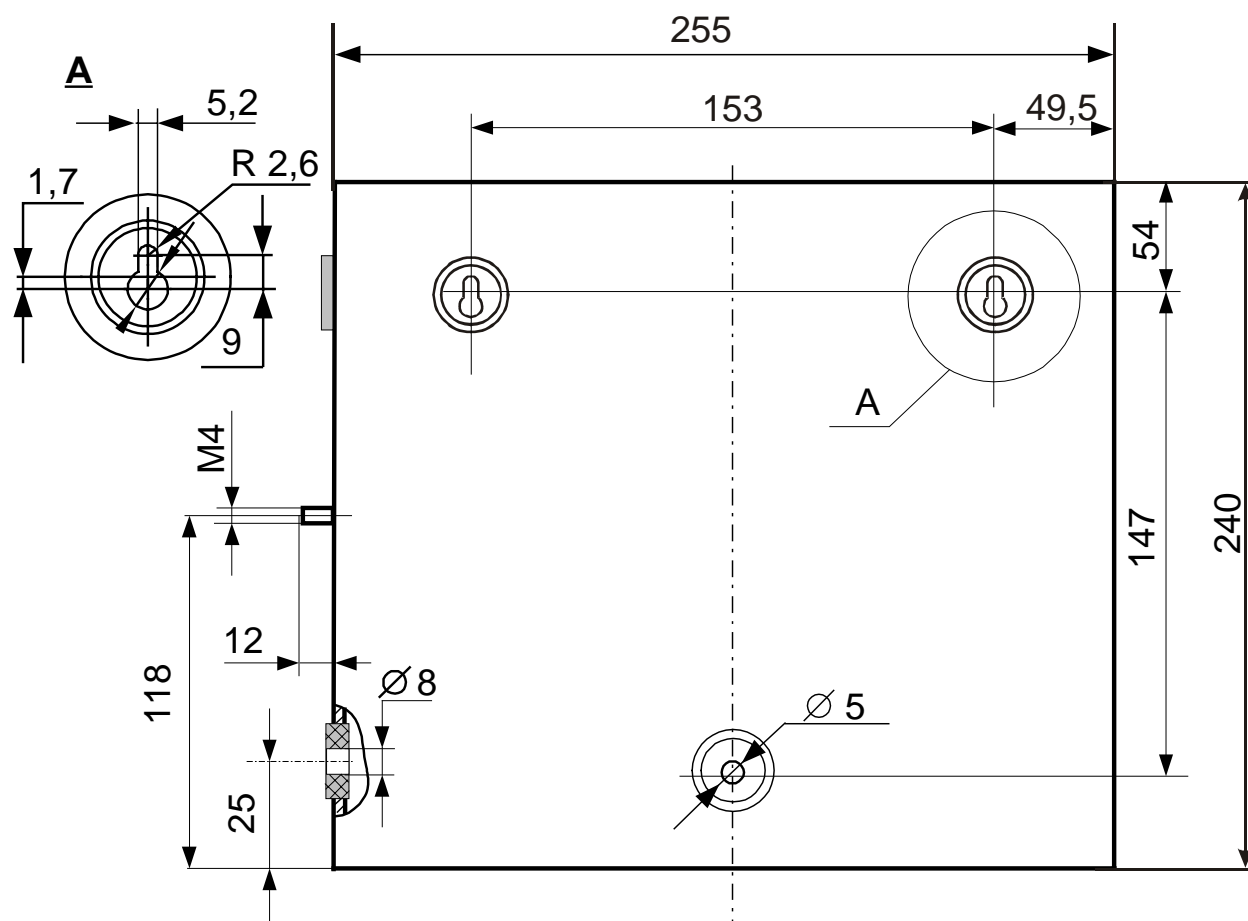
Габаритные и присоединительные размеры КА2 (исп. 1)
